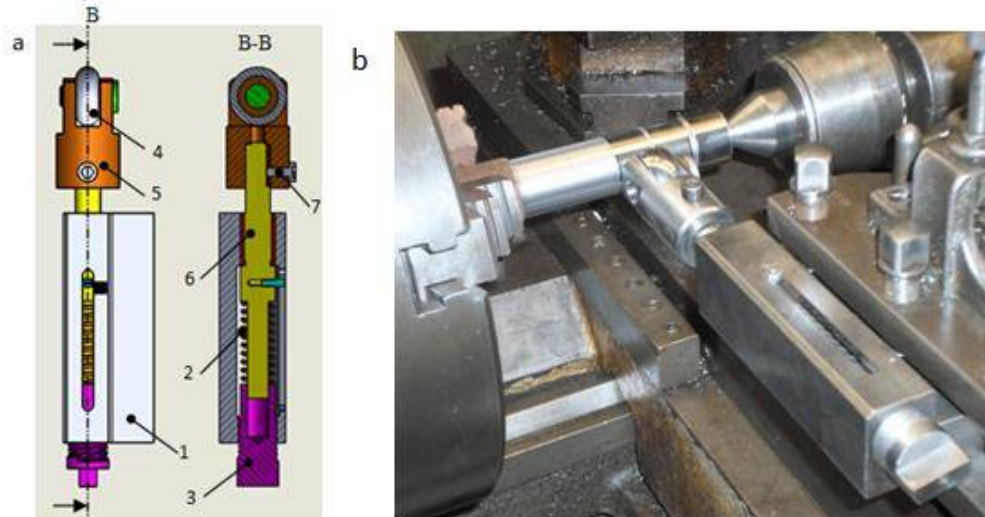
Outil de galetage, a) vue en coupe : 1- corps, 2- ressort, 3- tige filetée, 4- galet, 5- chape, 6- axe principal et 7- vis à six pans b) montage de l'outil sur le tour.
